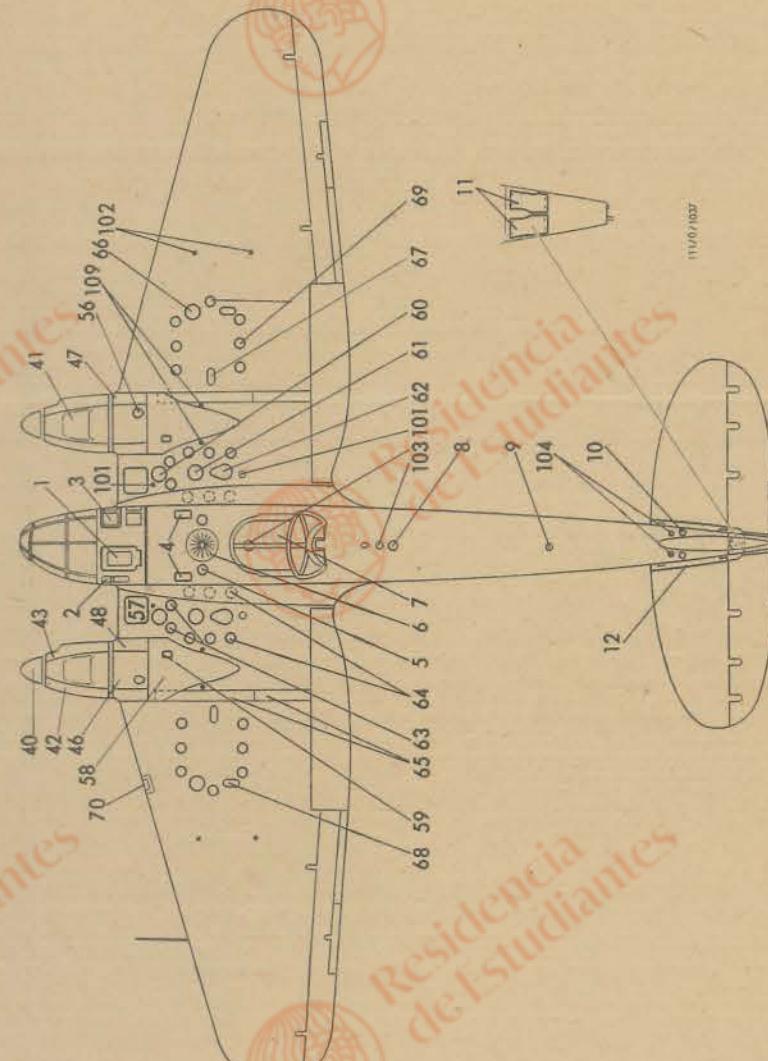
Deckel- und Klappenplan (Draufsicht)
